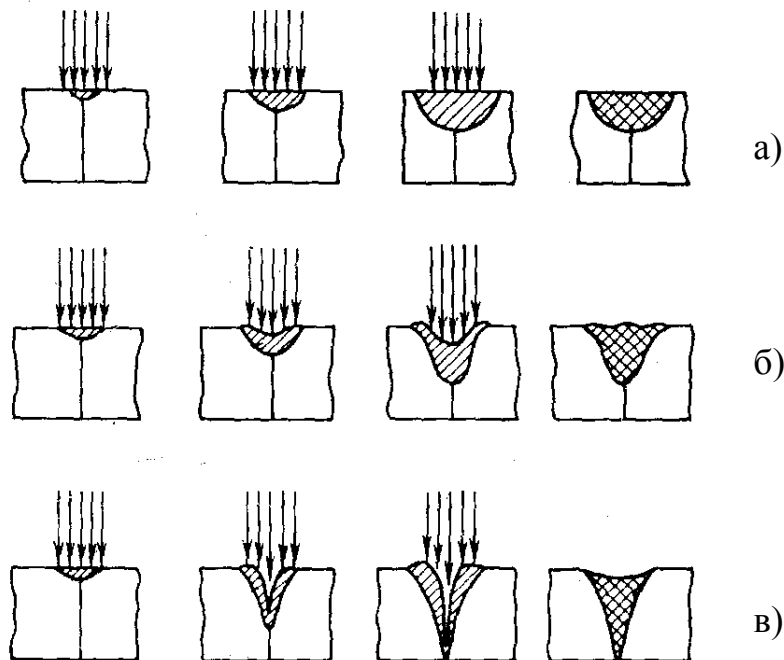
Режимы лазерной сварки: а) теплопроводный режим, б) сварка с прогибом, в) режим кинжального проплавления
